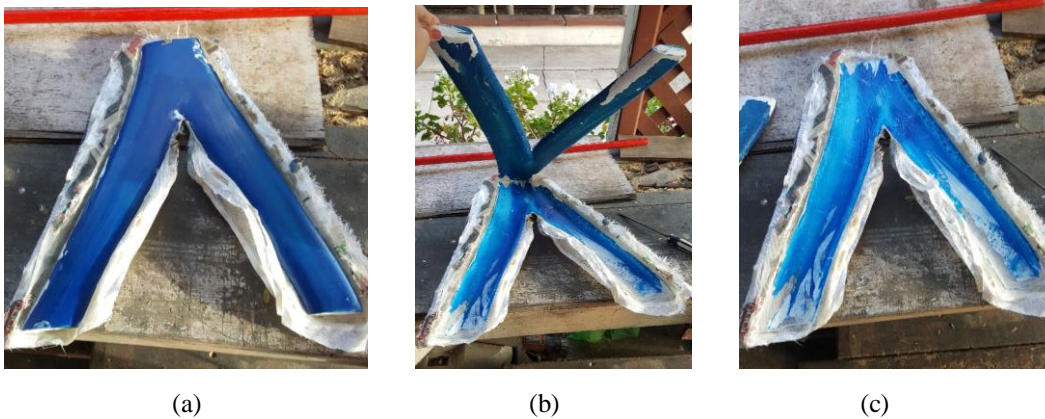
(a) Vista frontal posterior del modelo, (b) desmolde del modelo, (c) molde de la horquilla.
